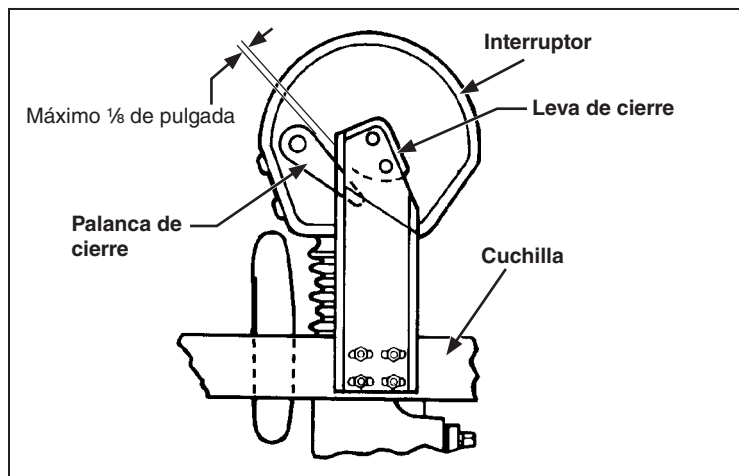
Conjunto de la cuchilla en posición de cierre total.
